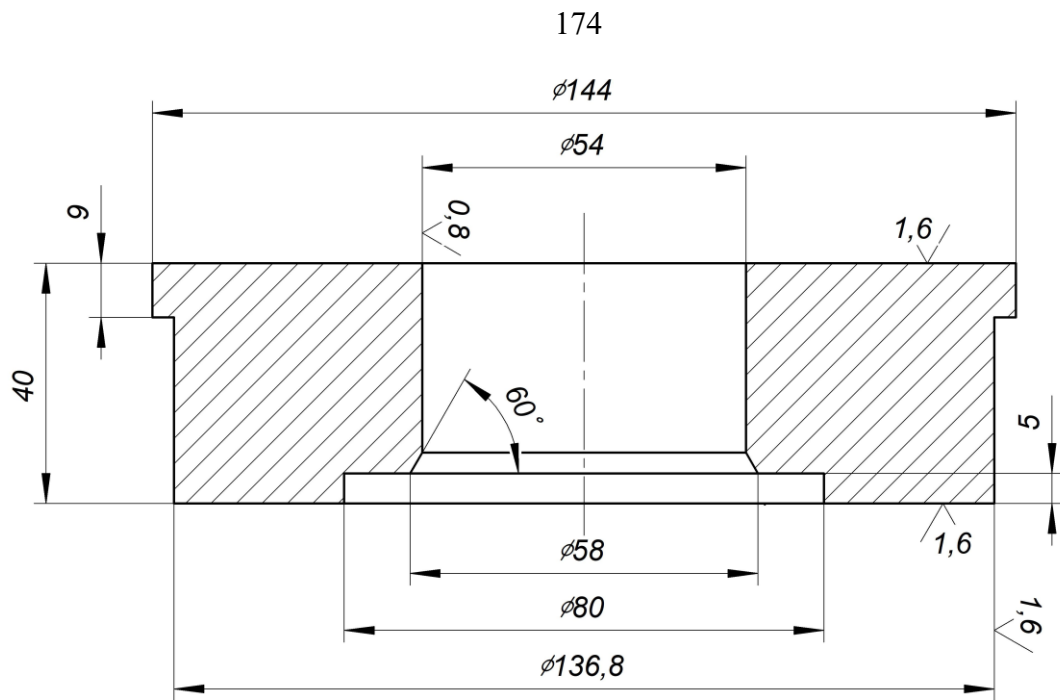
Чертеж выталкиватель (позиция 8)
